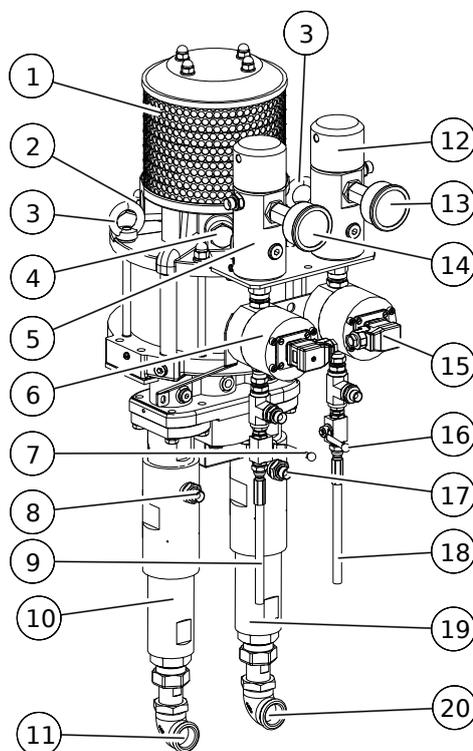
Dosierpumpe bei Ausführung mit Steuer-schrank
